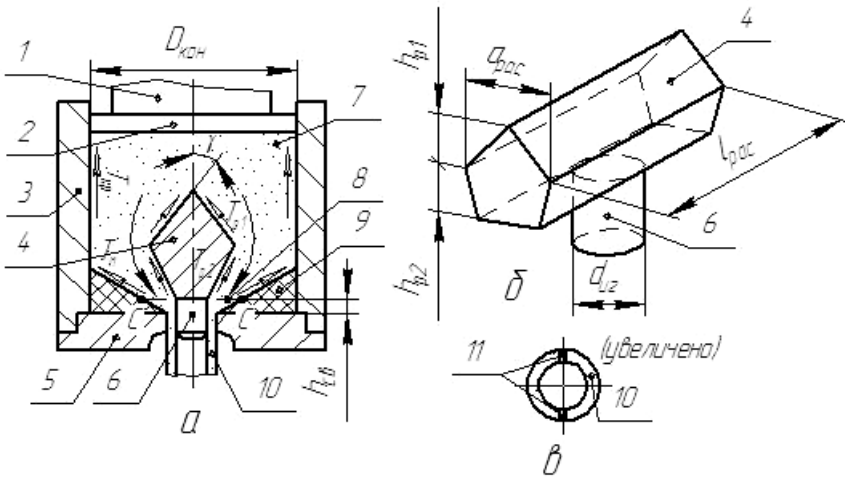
Схема прессования через матрицу с вмонтированной иглой: а – общий вид; б – рассекатель; в – изделие; 1 – пресс-штыпель; 2 – пресс-шайба; 3 – контейнер; 4 – выступающий рассекатель; 5 – матрица; 6 – игла; 7 – заготовка; 8 – "характеристическое сечение"; 9 – мертвая зона; 10 – изделие; 11 – сварные швы
